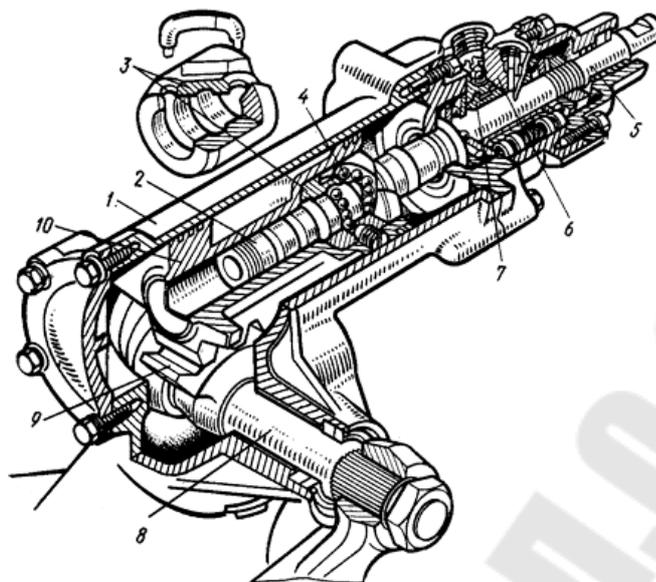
Устройство рулевого механизма с встроенным гидроусилителем
